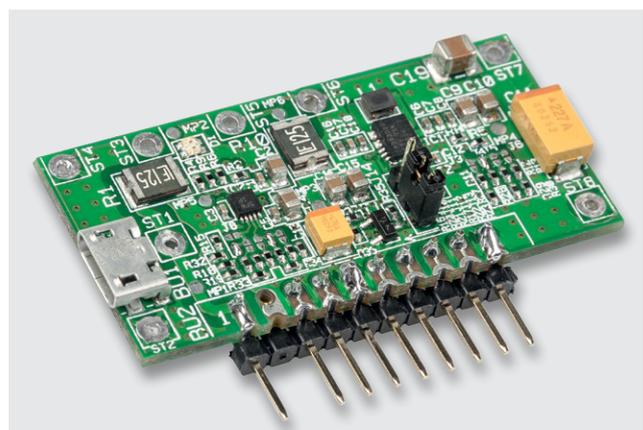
Alternative Bestückung mit einer abgewinkelten Stiftleiste für die komplette Kontaktierung
